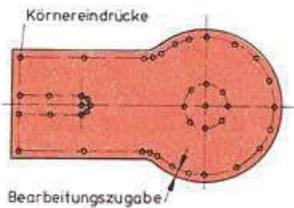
/14: Durch Körner gekennzeichnete Rißlinien
